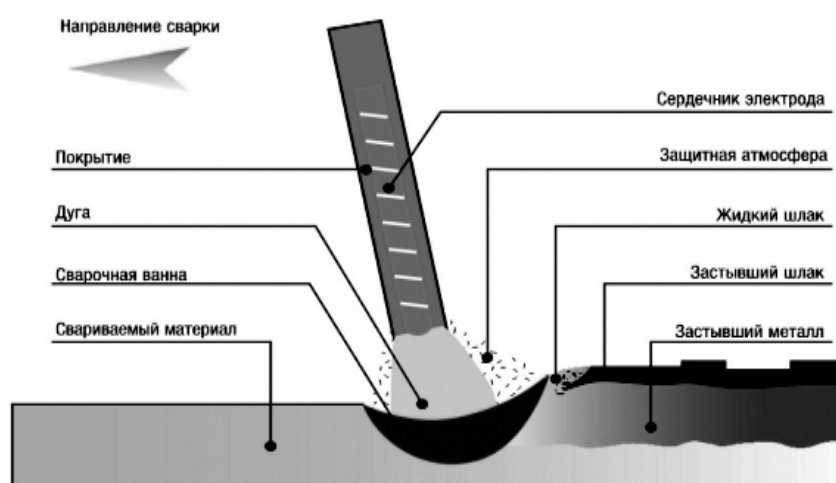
Схема ручной дуговой сварки
